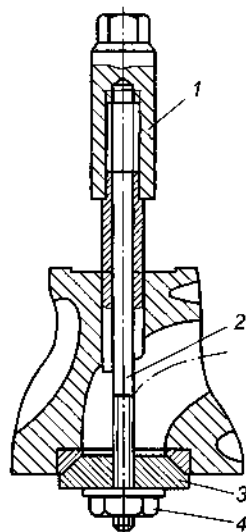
Запрессовка направляющей втулки с помощью винтового приспособления с опорой и центрированием по седлу клапана: 1 — толкатель; 2 — шпилька; 3 — опорная шайба; 4 — гайка
